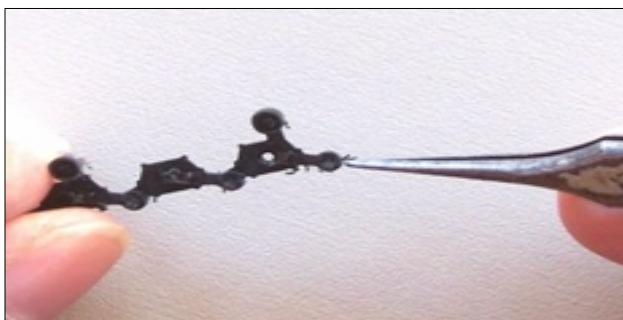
Bei Aufhängungsarmleisten die Frässpäne auszupfen
